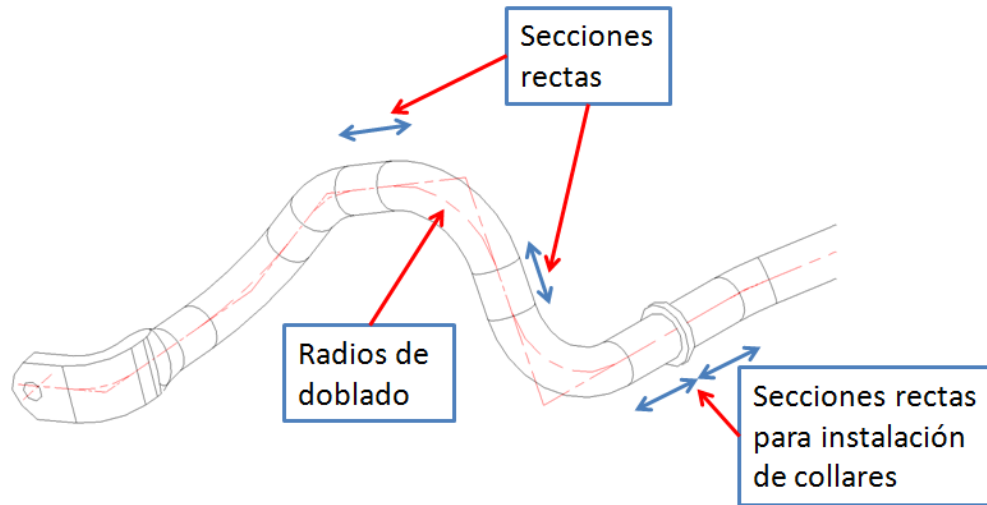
Restricciones geométricas de diseño de barras solidas.
